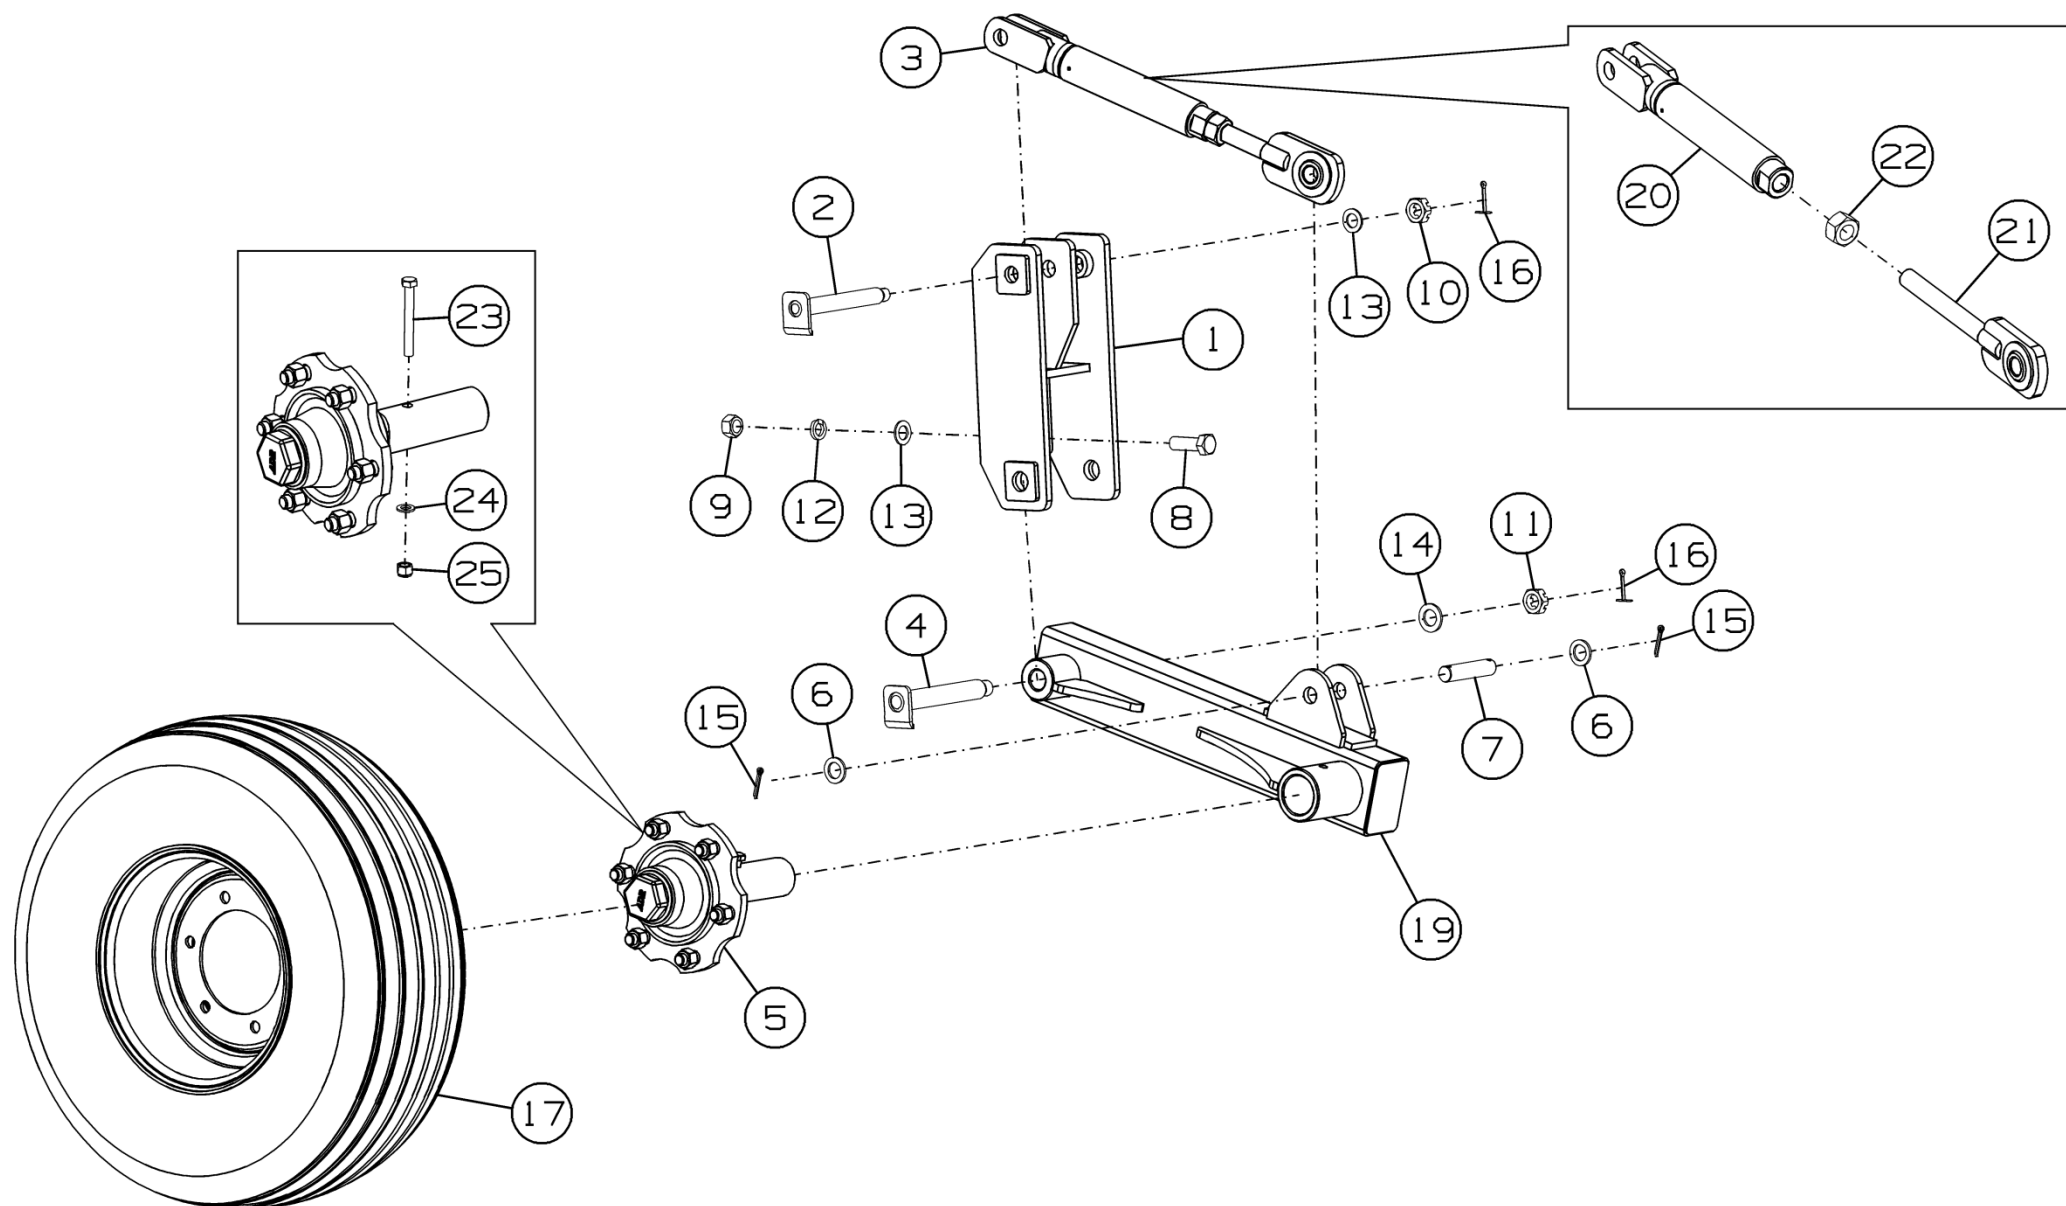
Колесо опорное СГ-122.06.000-01
